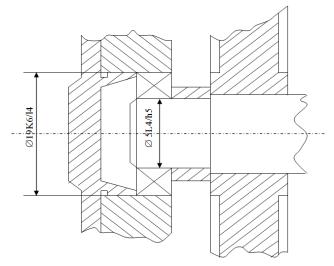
Эскиз сопряжения подшипника с валом и корпусом
